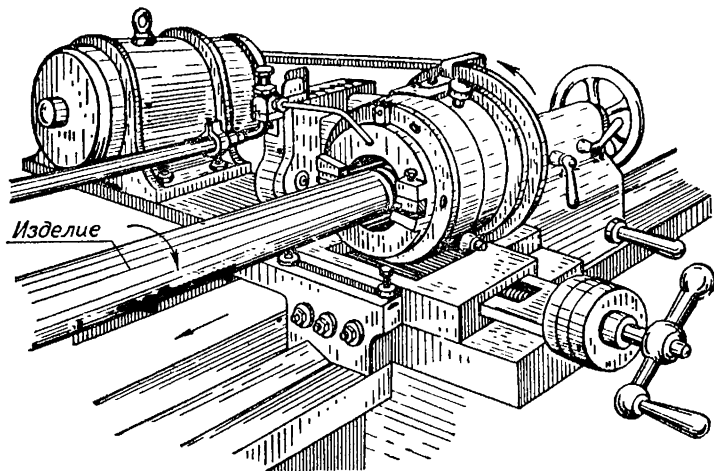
Общий вид приспособления к токарному станку для вихревого нарезания резьб
